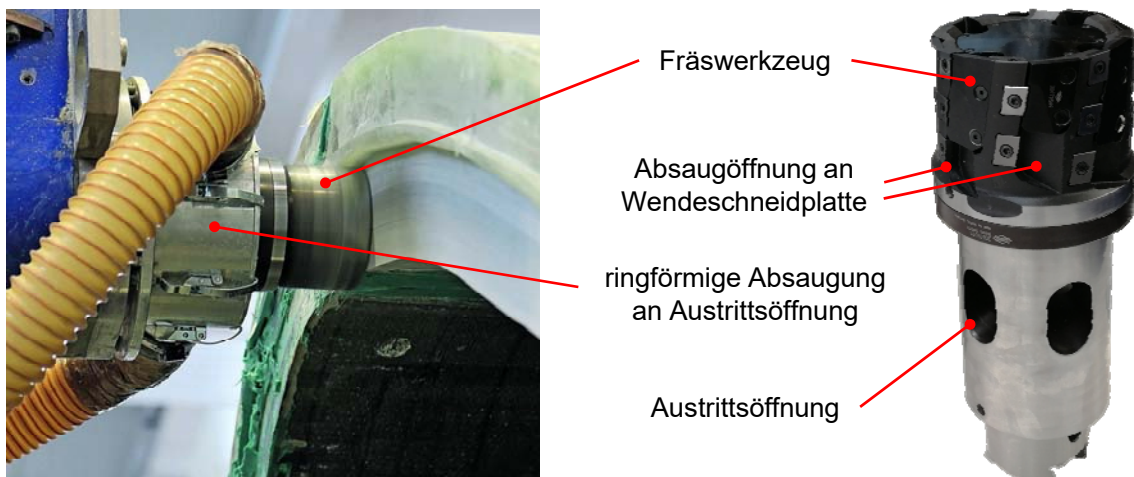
Innenabgesaugtes Fräs Werkzeug im Einsatz (links) (N. N. 2016) und im ausgebauten Zustand (rechts)
